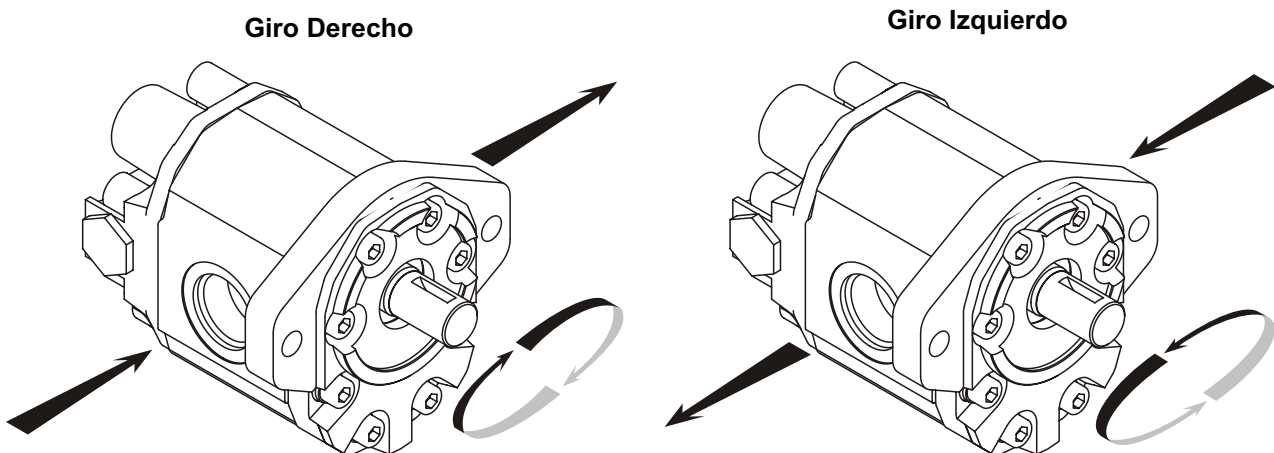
Identificación del sentido de giro de una bomba a engranajes
